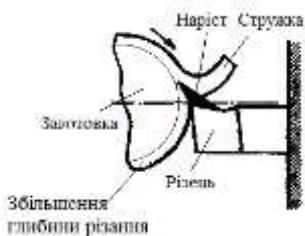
Схема впливу наросту на процес обробки лезовим інструментом
